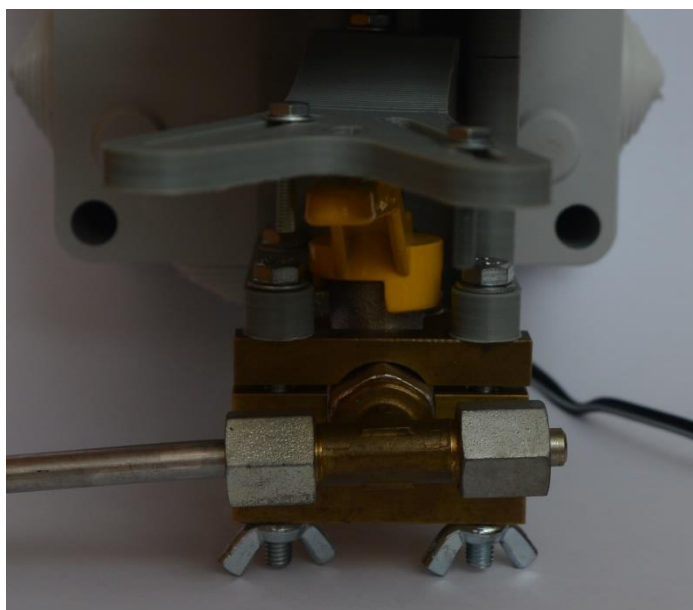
Zarovnání páky pohonu a ventilu před instalací
